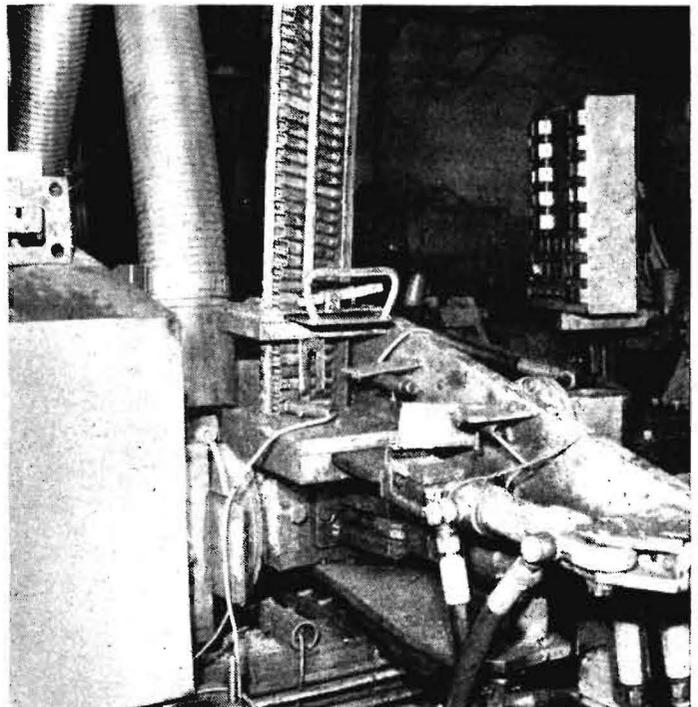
Randfinger-Schweißroboter, MBL-Schweißkopf und Fingermagazin (Fotos: E. Bräunlich)
